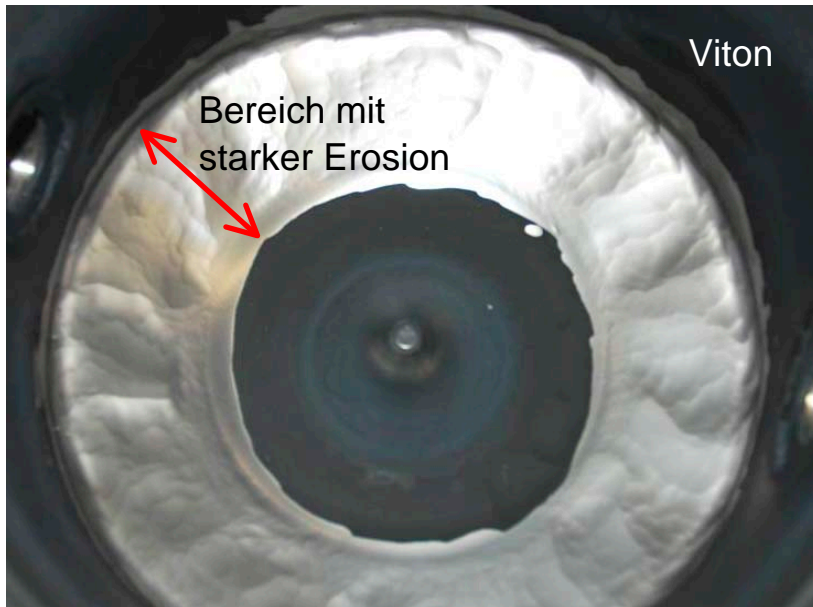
Erosiver Materialabtrag am eingeschweißten Behälterboden (Draufsicht)
